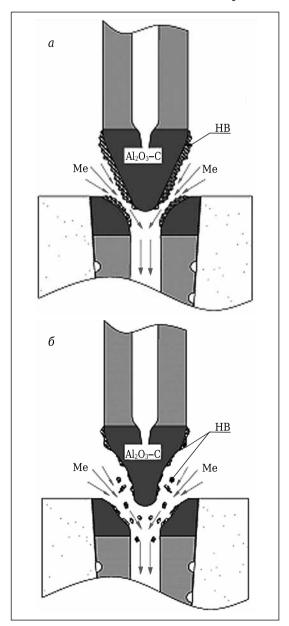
Система дозирования металла стопор-моноблок – стакан-дозатор при разливке заготовок: a — малых сечений; δ — больших сечений
